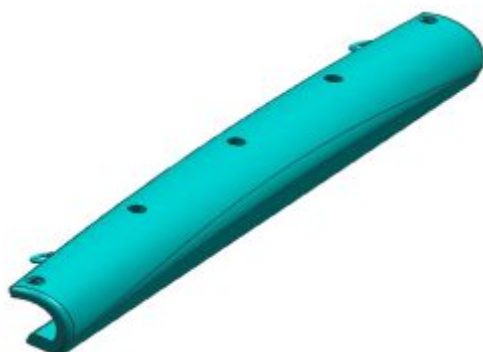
Конструкция дополнительного «клюва» зажима прессы
